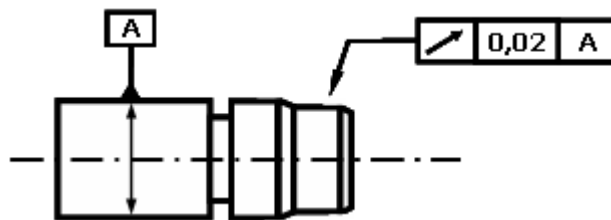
Indicação de tolerância de batida radial em desenho técnico
